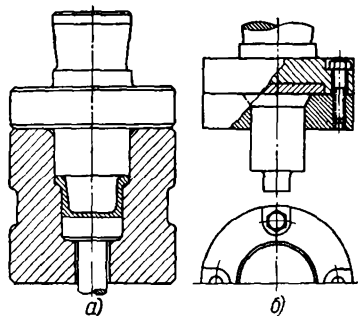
Рабочие детали закрытого штампа для круглой поковки: а — рабочие детали в сборе; б — вариант крепления пуансона
